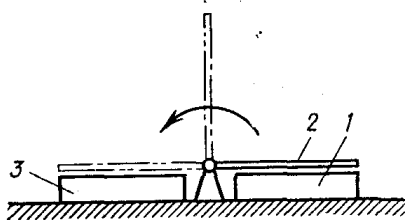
Схема устройства для сборки и сварки ферм
